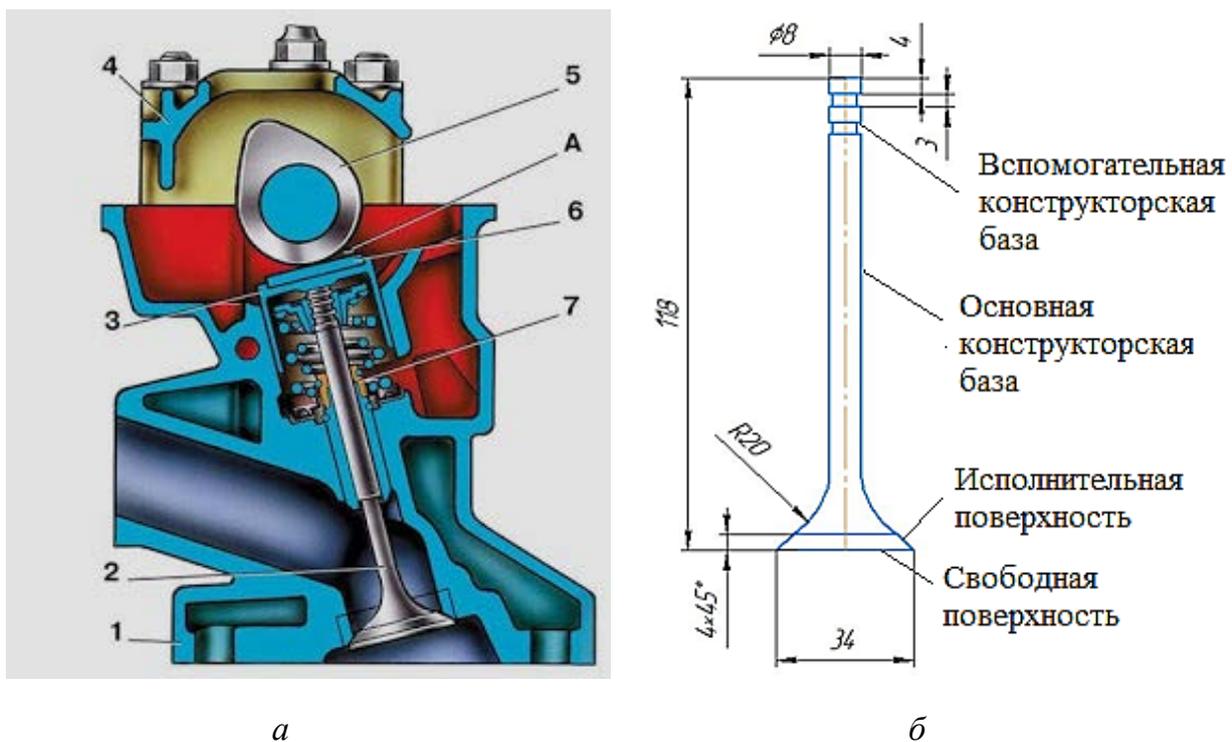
Механизм привода клапанов (а) и чертеж клапана (б)
